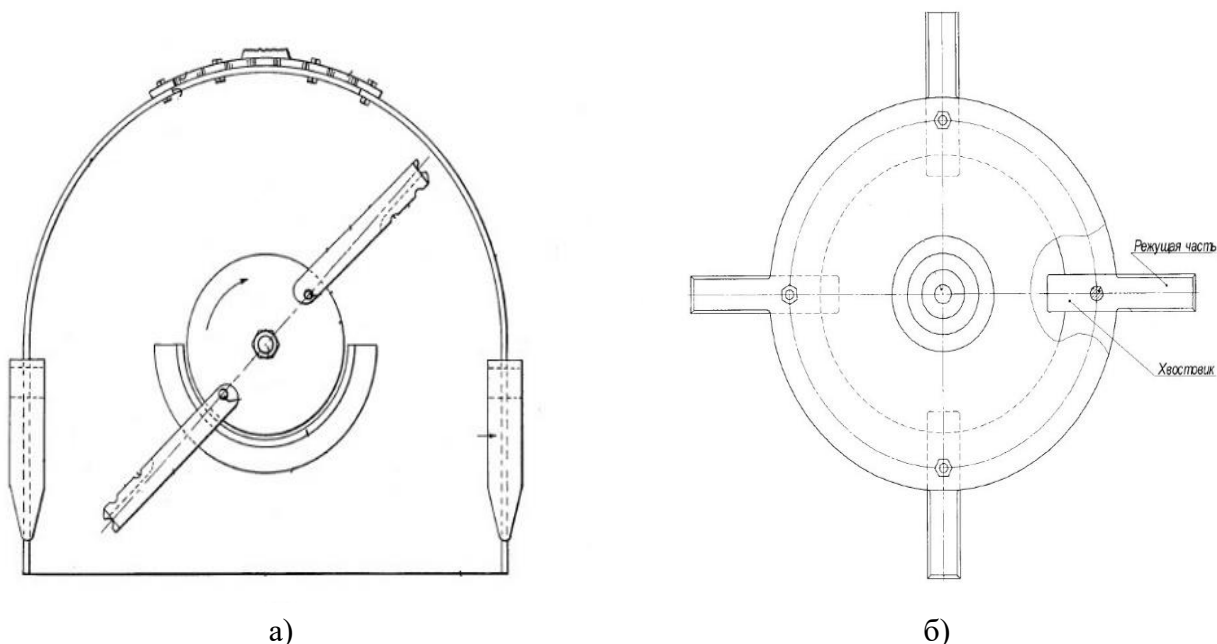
Ножевой шарнирно-сочленённый рабочий орган кустореза
